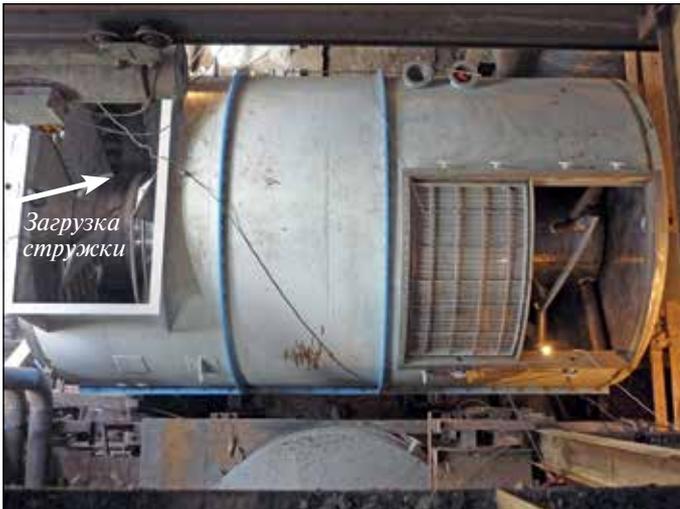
Противоточный ошпариватель во время монтажа (вид сверху)
